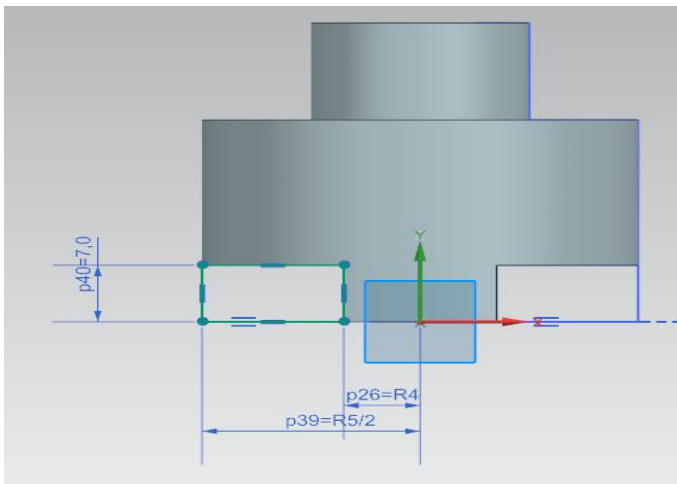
Замена размеров формулами для детали «VTULKA2»
